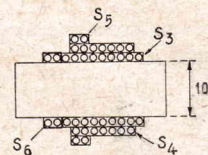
Disposition des bobinages du circuit oscillateur.
